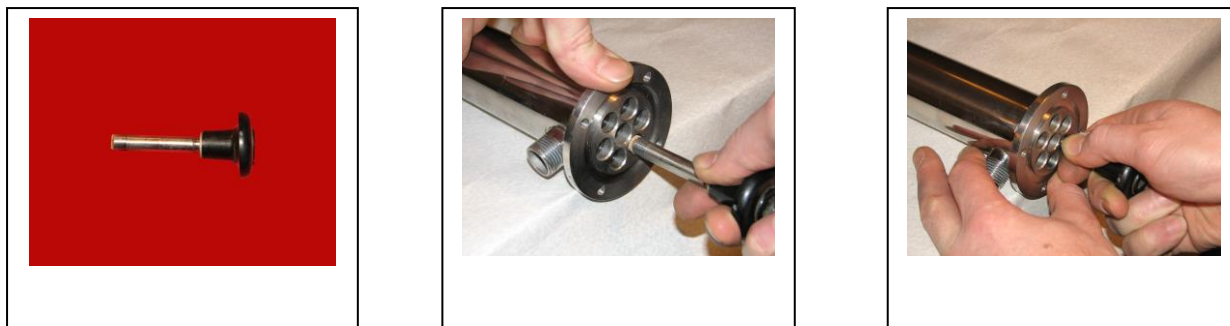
Установка уплотнительных колец: а – вид приспособления; б - 1<sup>я</sup> фаза «вдавливания» уплотнительного кольца; в - 2<sup>я</sup> фаза «вдавливания» уплотнительного кольца
